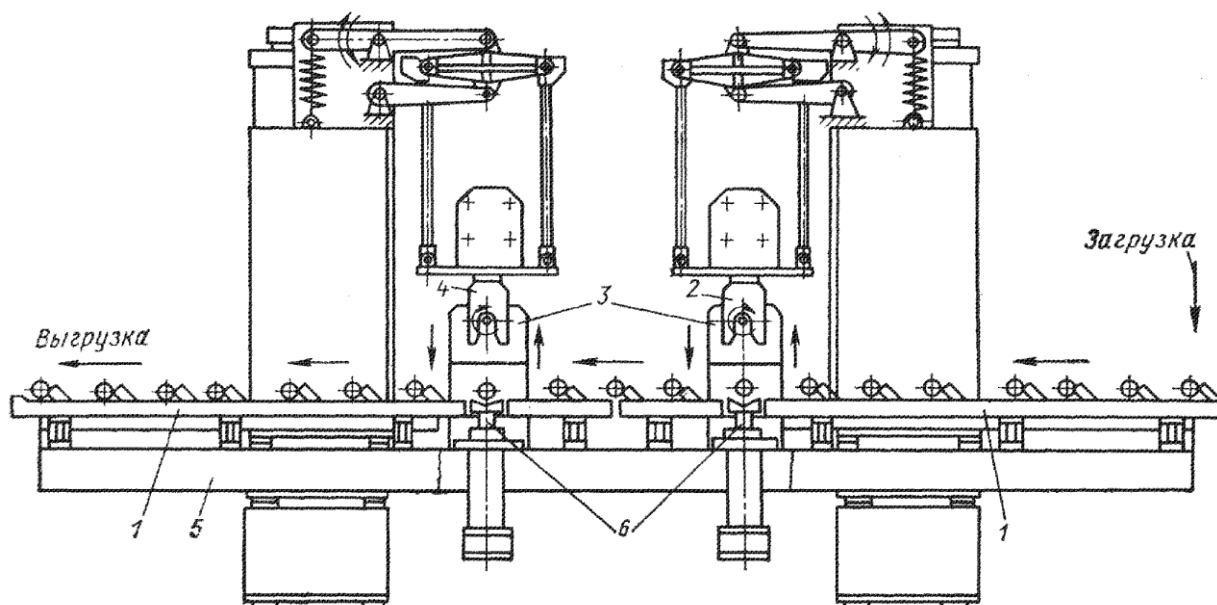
Схема установки для закалки шеек коленчатых валов ТВЧ
